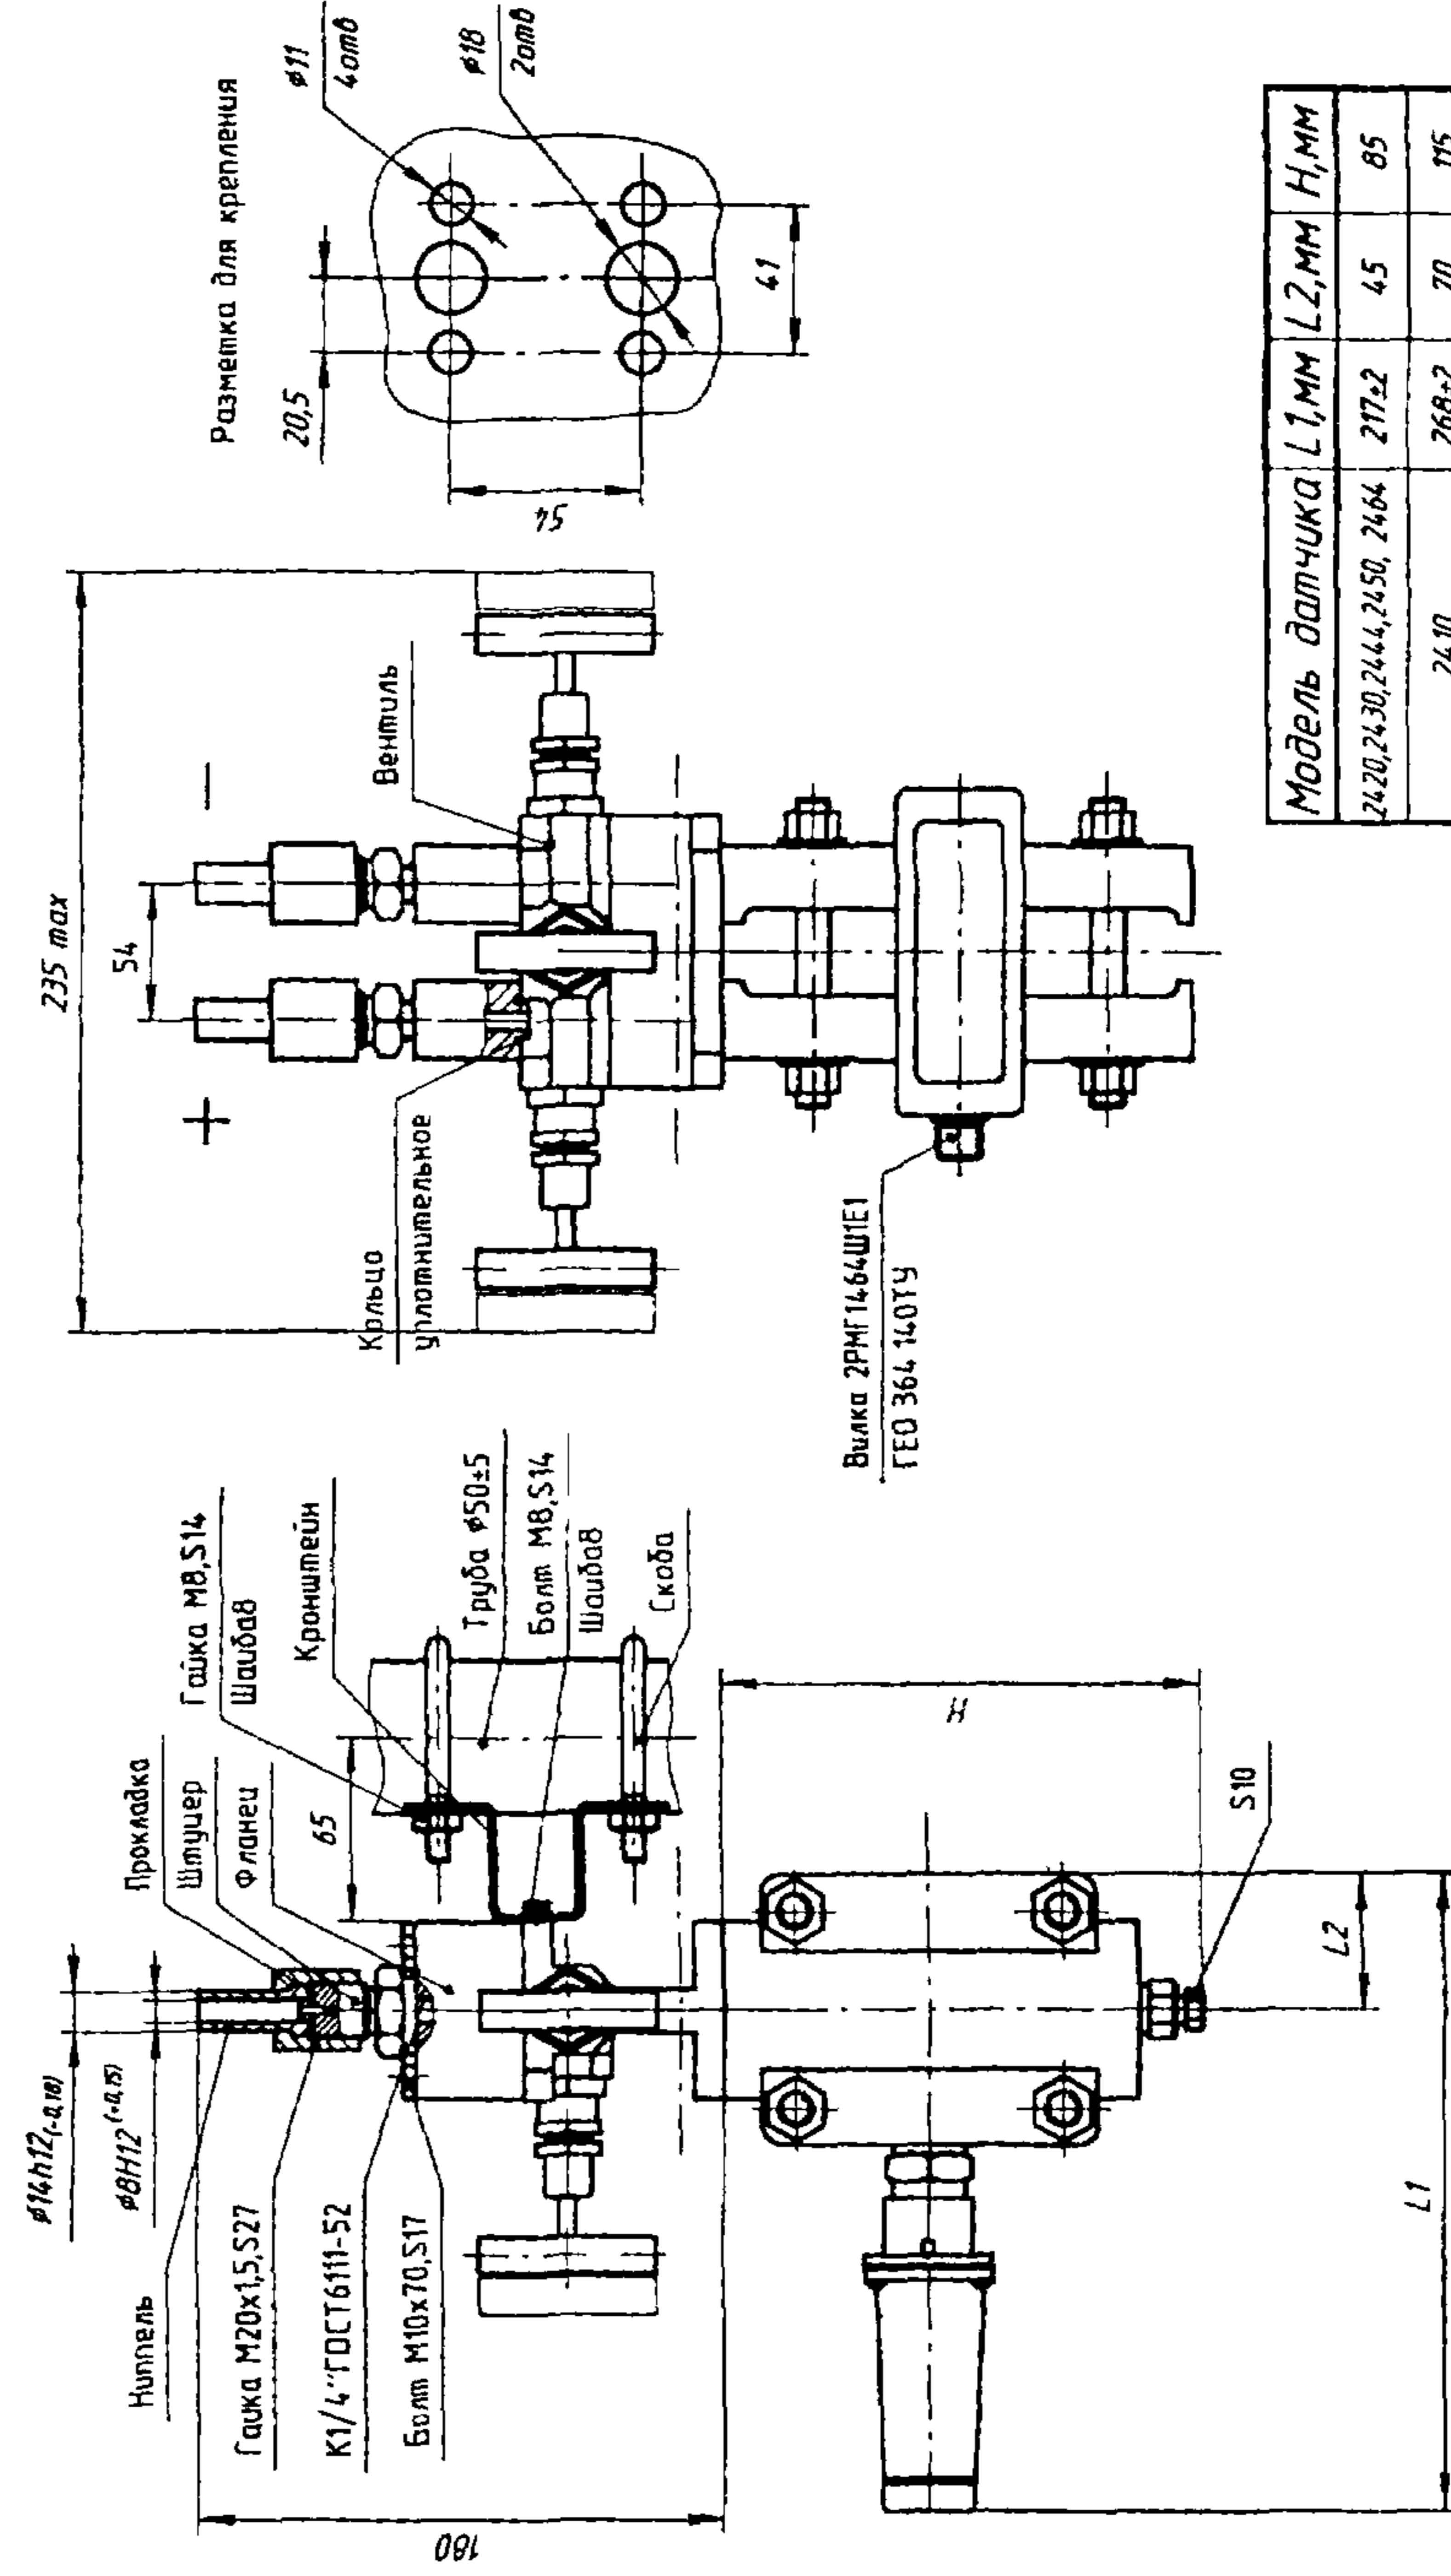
Установочные и присоединительные размеры датчиков моделей 2410, 2420, 2434, 2444, 2450, 2464 с установленным фланцевым трехвентильным блоком, ниппелями под накидные гайки
